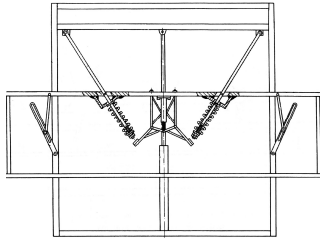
Схема пружинной V-образной маятниковой навески штанги опрыскивателя [38, 78]
